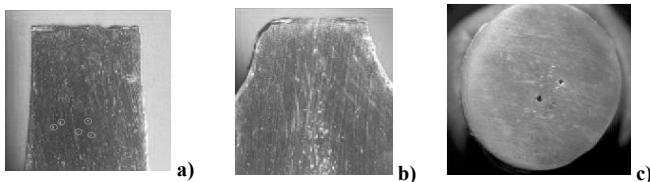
Makroskopische Darstellungen der Porosität der Mg-Legierung AE42 in unterschiedlichen Ansichten: a) Längsschnitt einer glatten Probe, b) Längsschnitt einer gekerbten Probe und c) Querschnitt einer glatten Probe. Die Poren sind makroskopisch sichtbar und überwiegend innerhalb eines zentralen Bereichs des Probenquerschnitts konzentriert.
